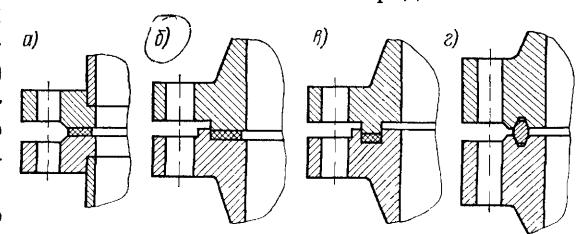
38. Типы уплотнительных поверхностей фланцевых соединений a — гладкая уплотнительная поверхность; δ — выступ-впадина; ϵ — шип-паз; ϵ — под металлическую прокладку
